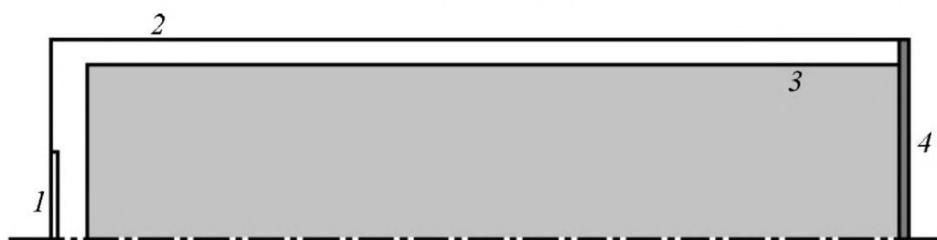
Внешний вид изделия: 1 – инициирующее устройство, 2 – корпус, 3 – таблетка-излучатель, 4 – мембрана
